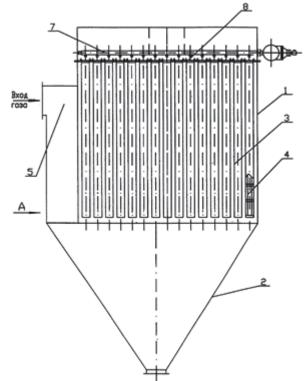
Общий вид рукавного фильтра для очистки газа:
